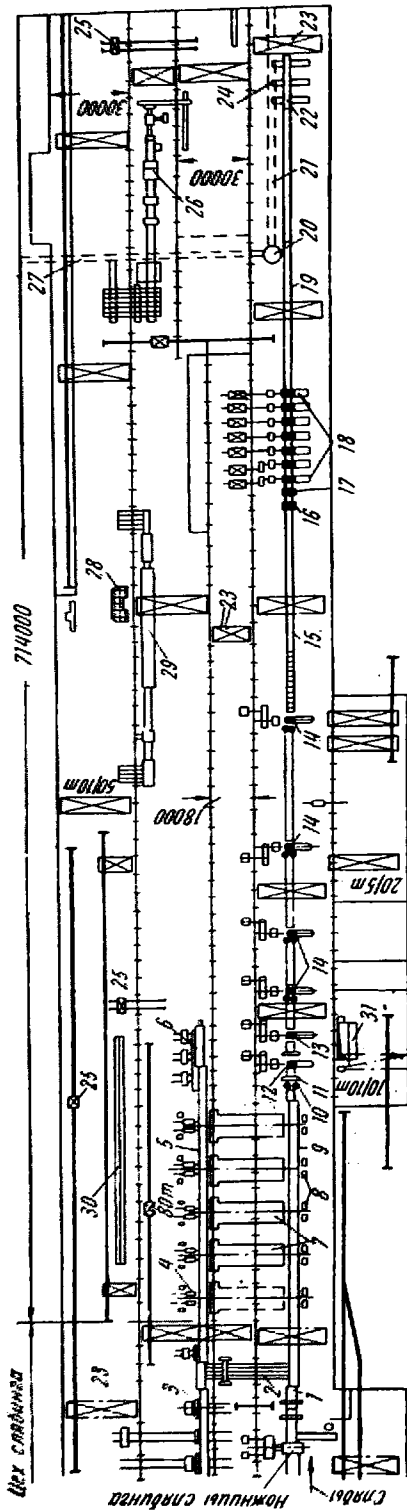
Схема расположения оборудования непрерывного листового стана 1700:
